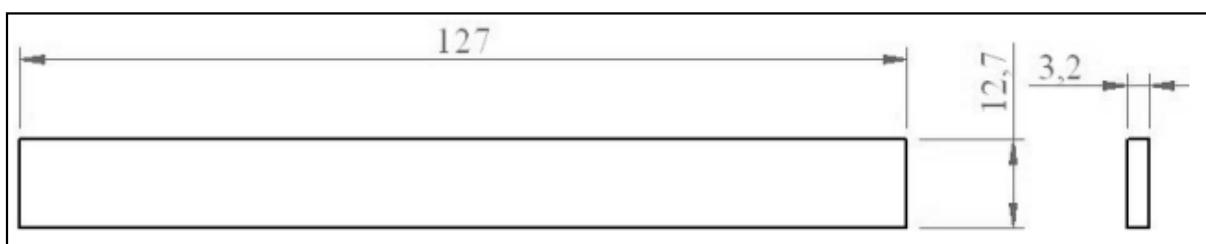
Dimensões do corpo de prova de flexão [mm]
